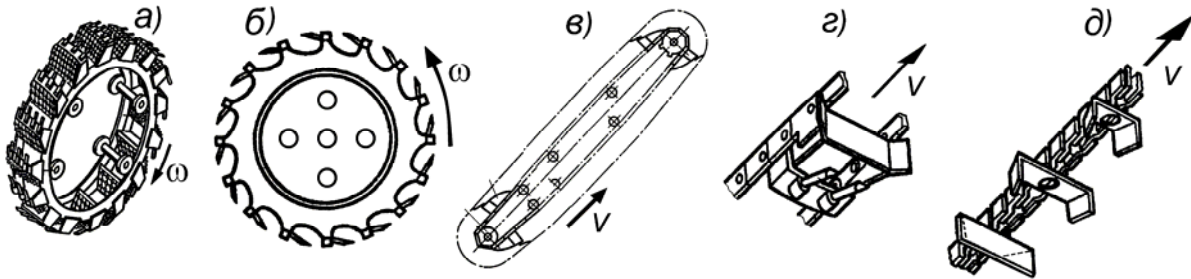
Рабочие органы экскаваторов непрерывного действия: а – роторный ковшовый; б – роторный фрезерный; в – цепной ковшовый; г и д – цепные скребковые
